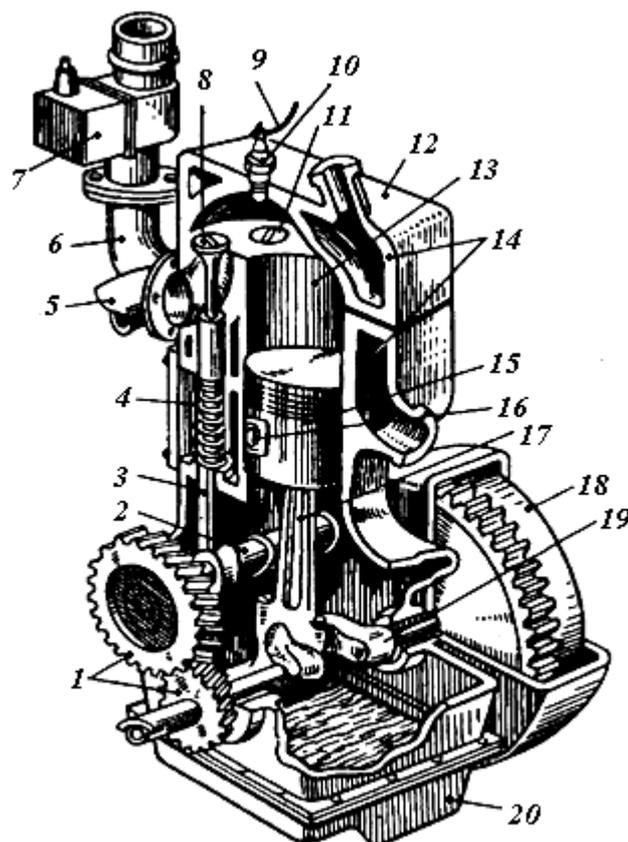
Устройство одноцилиндрового четырехтактного карбюраторного двигателя:
